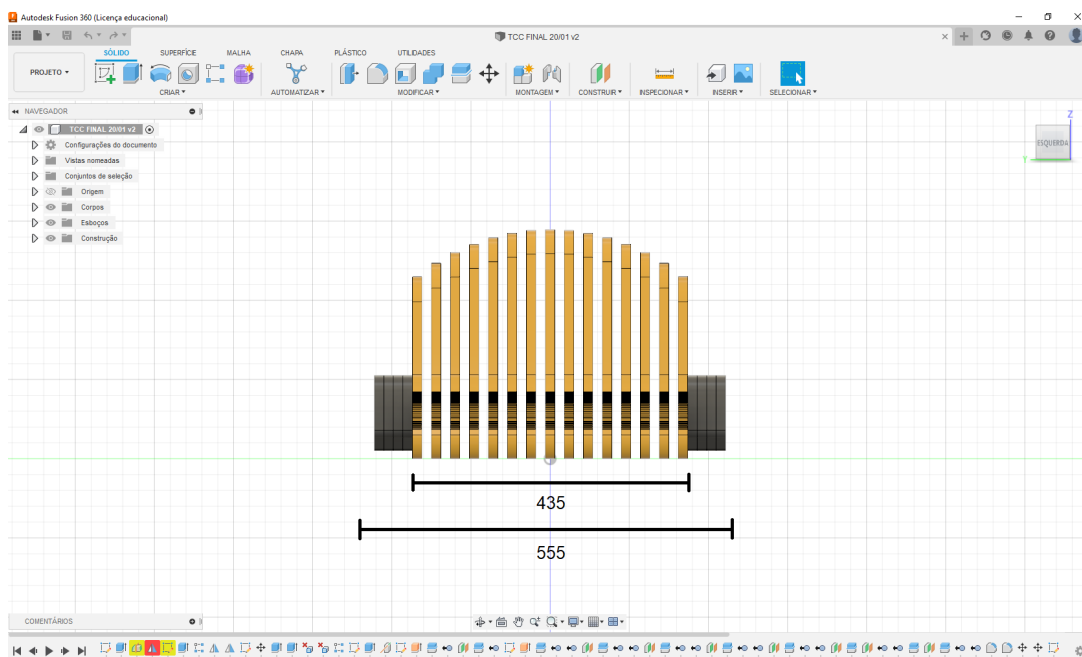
Vista frontal da cadeira a ser fabricada.
